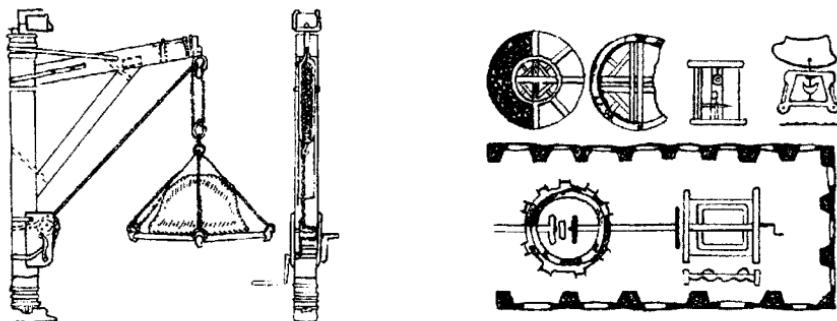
Чертежи Ф. Борзова и Р. Глинкова
